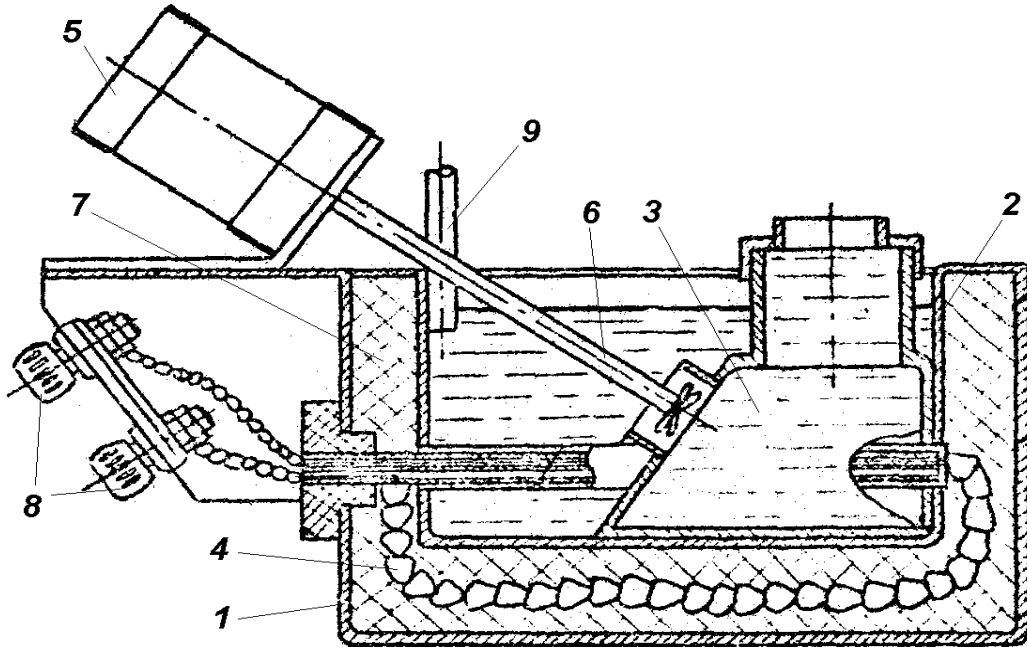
Конструкция лабораторной установки для пайки волной припоя:
